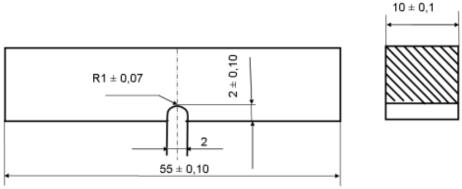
Стандартный образец с U-образным надрезом для испытаний на ударный изгиб
